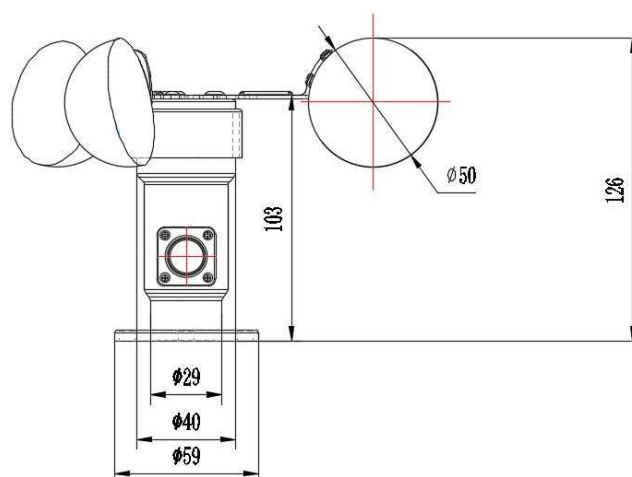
Размеры датчика скорости ветра ICB100-01
